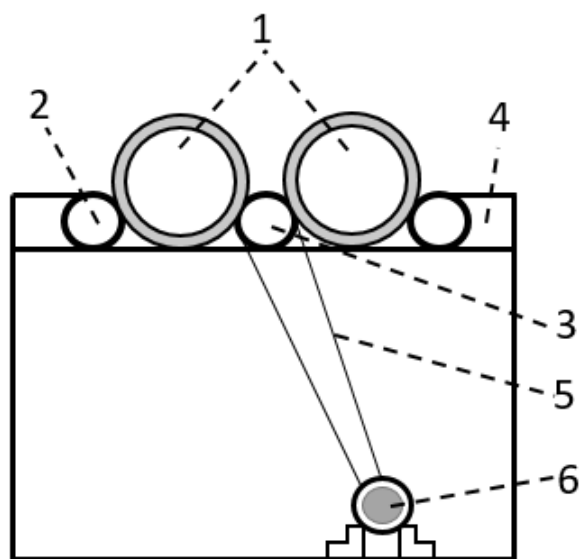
Схема установки шаровых мельниц: 1) Барабаны шаровых мельниц; 2) Поддерживающие валы; 3) Приводной вал; 4 – Станина; 5 – Клиноременная передача; 6 – Электродвигатель
